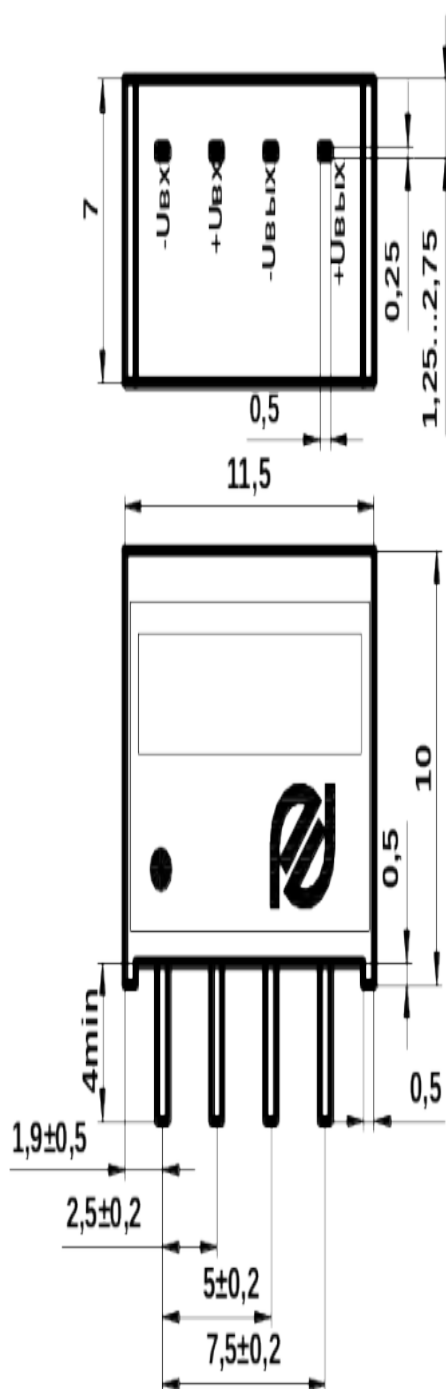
Габаритный чертеж модулей в корпусе «Е»
